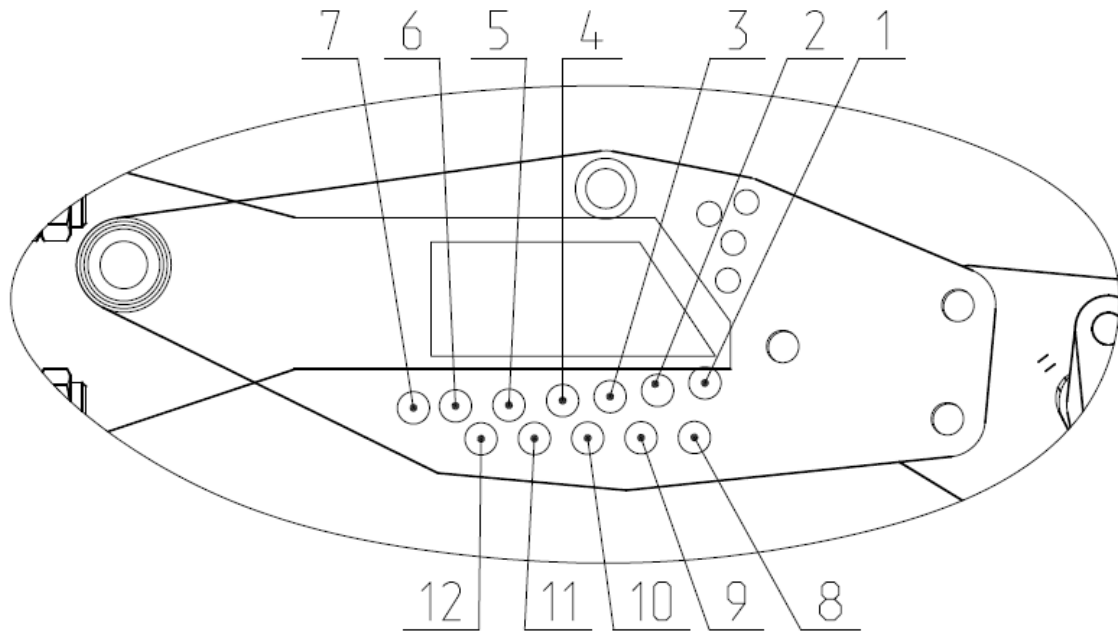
Установка глубины обработки рабочих органов катками двухрядными.
